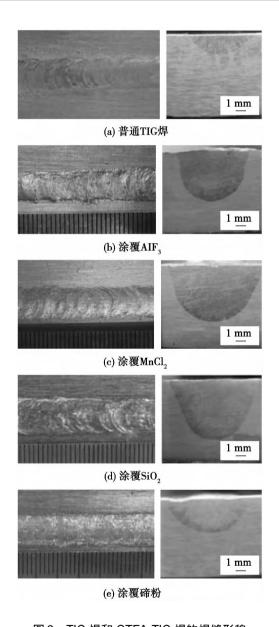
TIG 焊和 GTFA-TIG 焊的焊缝形貌 Fig. 2 Weld appearances of TIG and GTFA-TIG welding
